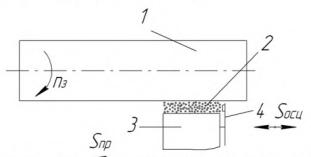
Схема магнитно-абразивной обработки с наложением ультразвуковых колебаний: 1 — обрабатываемая деталь; 2 — ферроабразивный порошок; 3 — полюсный наконечник; 4 — пружинная пластина
